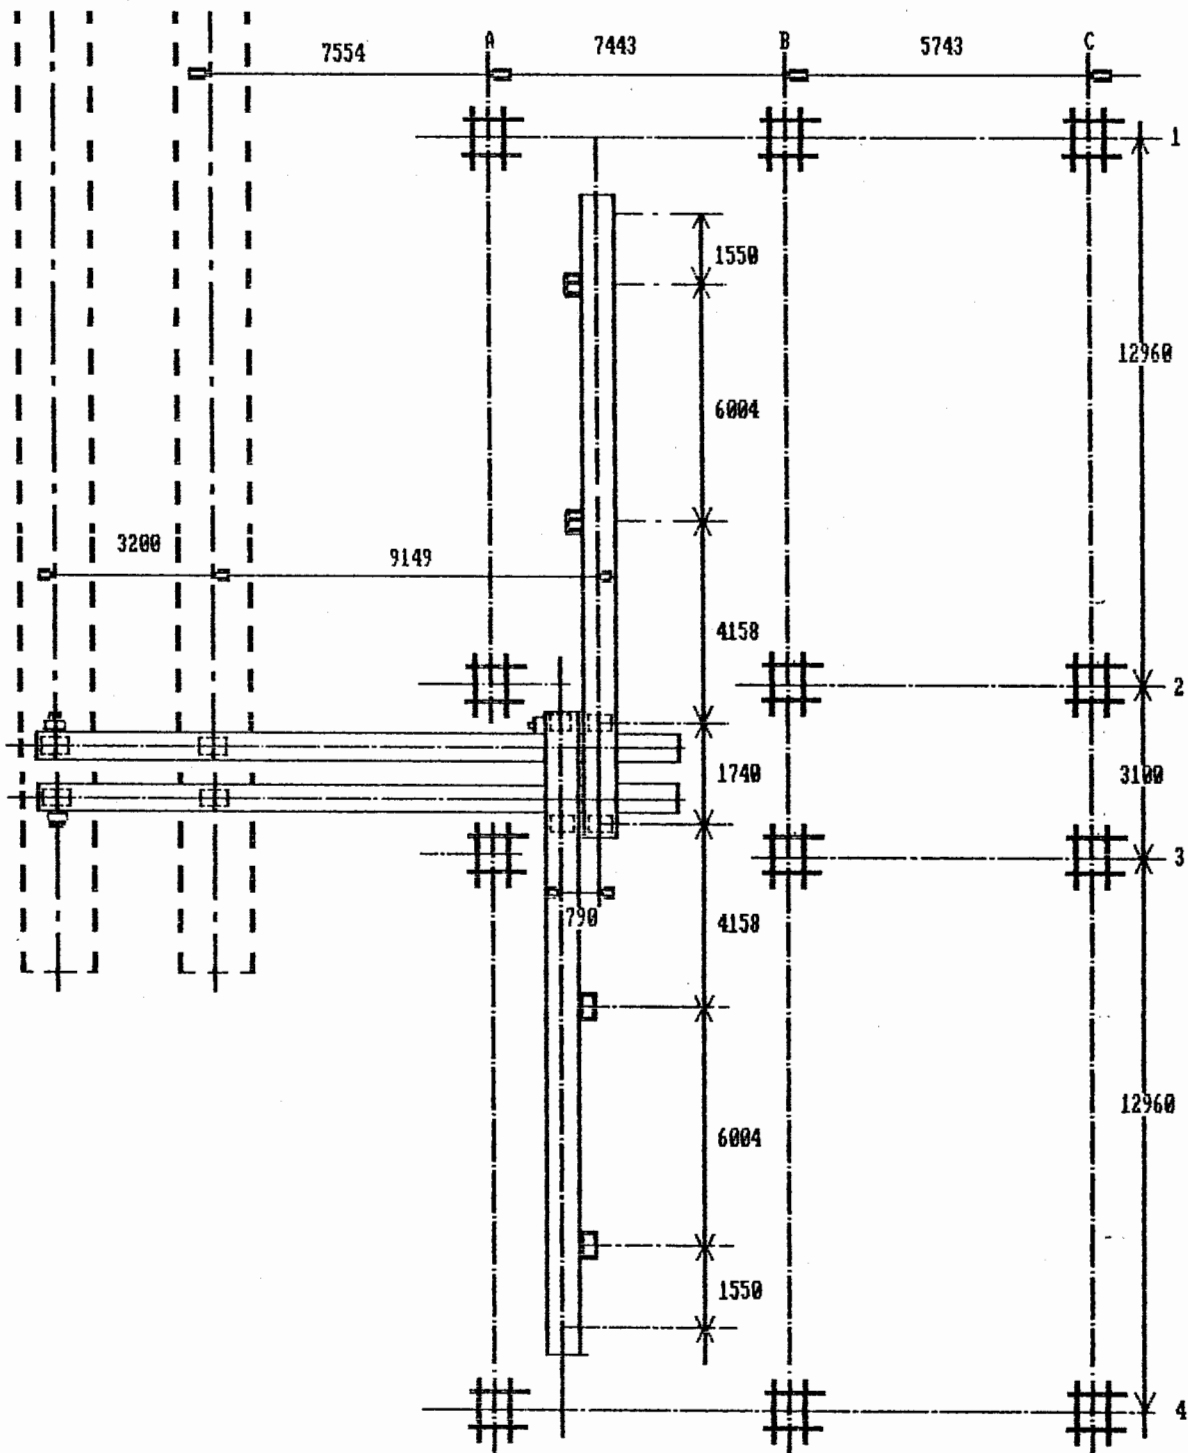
VISTA DE PLANTA DE LA DISPOSICION DE LAS BASTRAS TRANSPORTADORAS EN EL SISTEMA.
